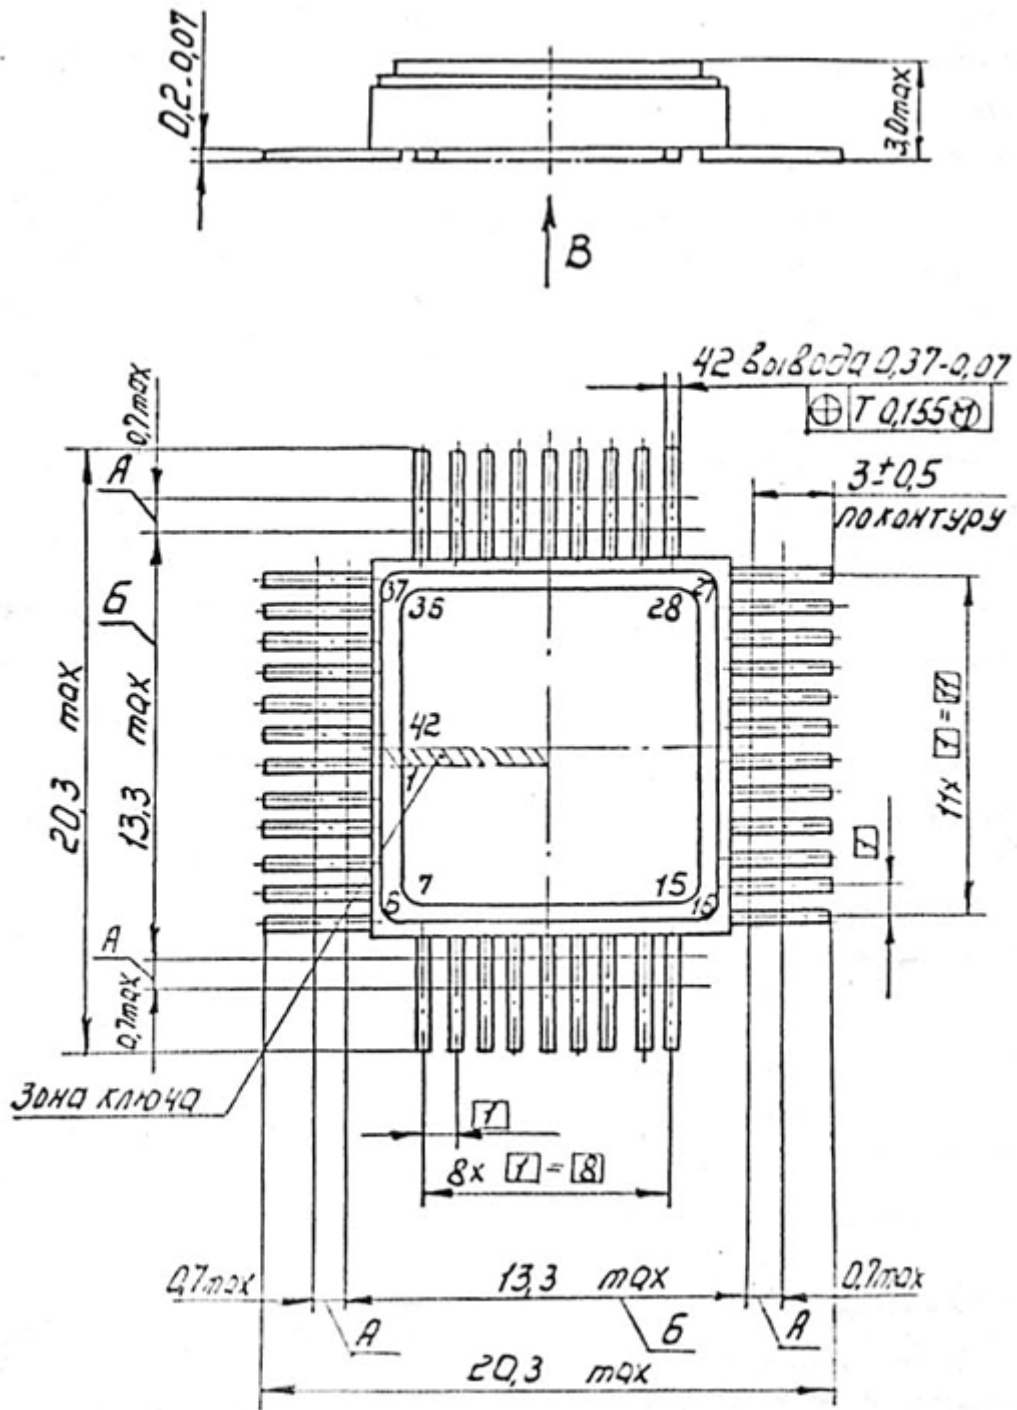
Габаритный чертеж корпуса Н14.42-1В
